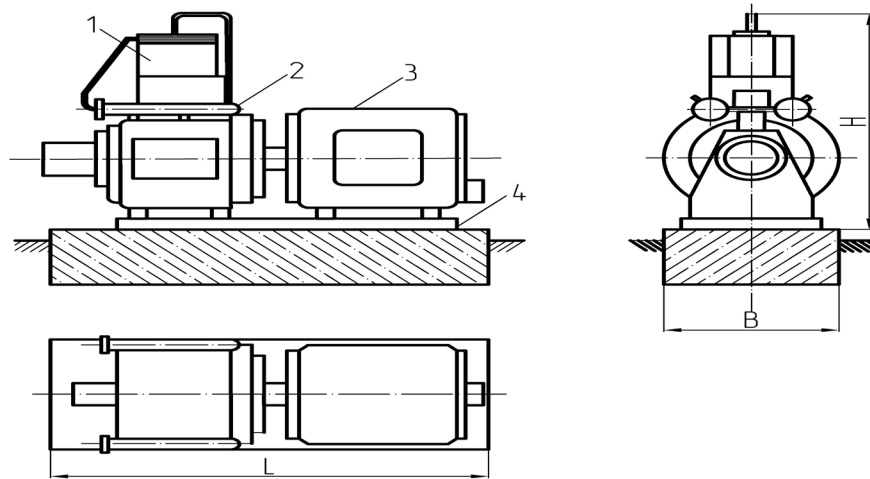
Габаритні розміри компресора: 1 – компресор;
